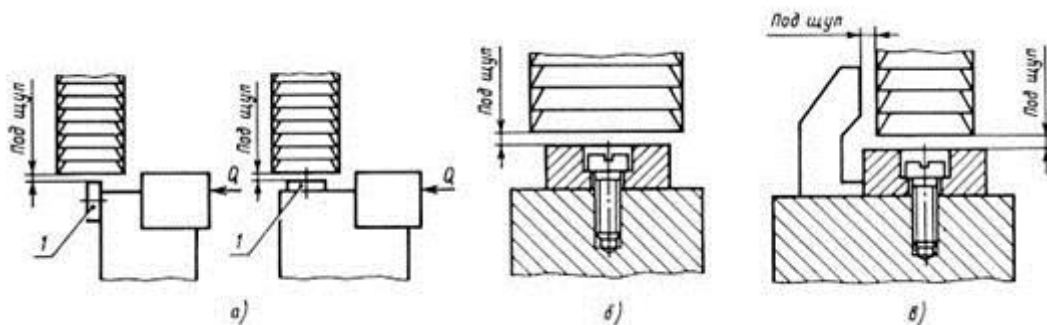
Шаблоны для токарных и фрезерных станков:
